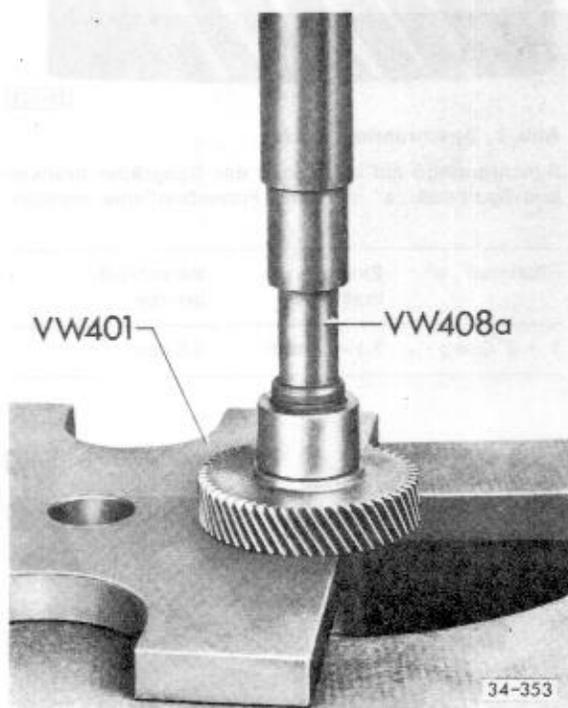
Zahnrad für 4. Gang mit Innenlauftring/Nadel-lager abpressen
